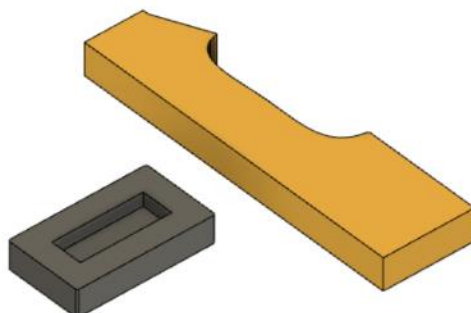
Visualização tridimensional de componentes de troféu para fresagem CNC. Fonte: Autora ,2023.
